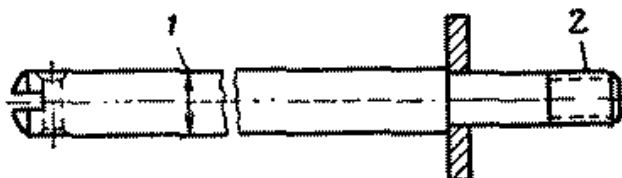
Толкатель поршня цилиндра гидровакуумного усилителя тормозов
